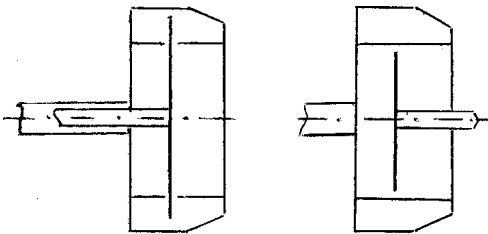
Робочі колеса вентиляторів з пересувними дисками
